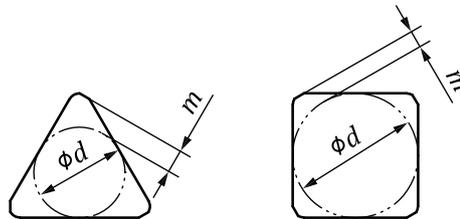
Cas 3: Plaquettes avec arêtes de planage (voir Note 1 du Tableau 9)
